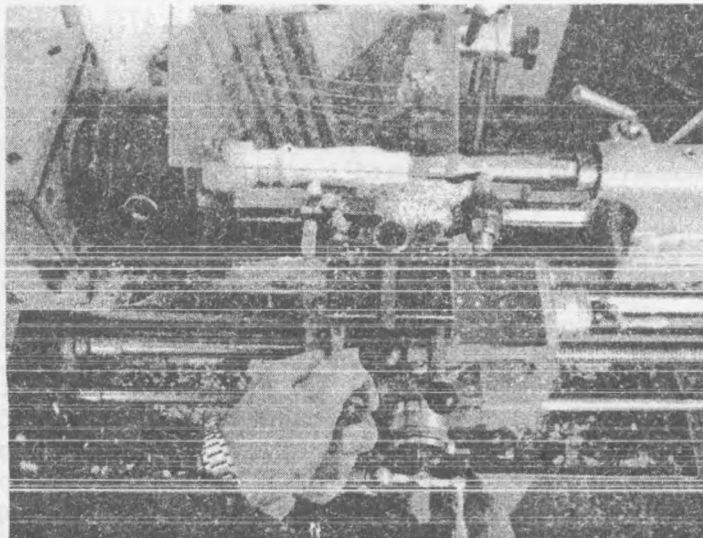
Процес точіння рукоятки для напилка за допомогою копіювального пристрою
